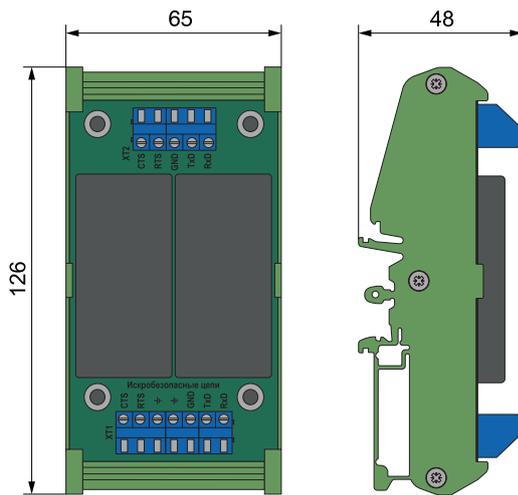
Габаритные размеры барьера ЭНИ-БИС-116-Ex-DIN
